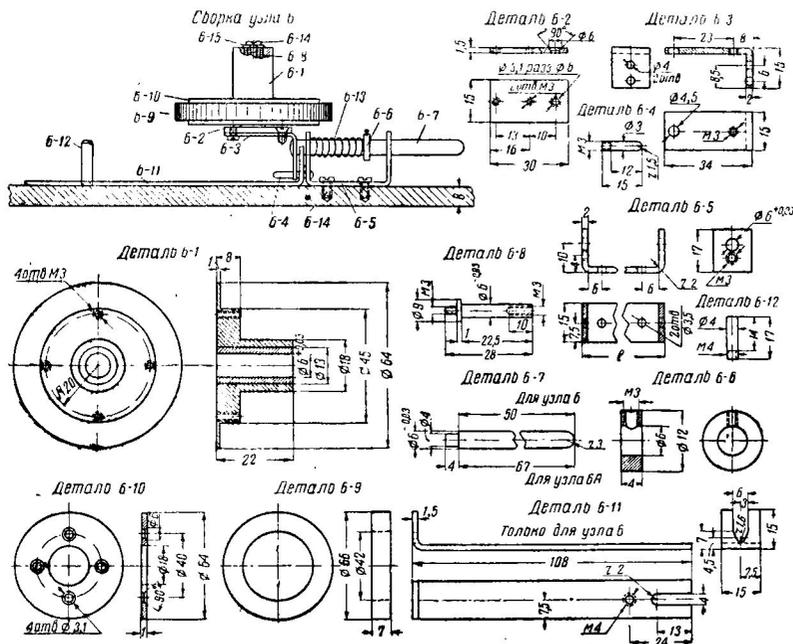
Паразитный ролик рабочего хода (узел 6) и перемотки (узел 6А) и его детали: 6-1—корпус ролика (дюралюминий Д16Т)—1 шт.; 6-2—подвижная площадка (сталь 20)—1 шт.; 6-3—уголок (сталь 20)—1 шт.; 6-4—направляющий стержень (сталь 45)—1 шт.; 6-5—скоба (сталь 20)—1 шт.; для узла 6  $l=32$  мм и для узла 6А  $l=65$  мм; 6-6—кольцо стопорное (сталь 25)—1 шт.; 6-7—стержень (сталь 45)—1 шт.; 6-8—ось паразитного ролика (сталь У8А)—1 шт.; 6-9—кольцо резиновое—1 шт.; 6-10—кольцо (дюралюминий Д16Т)—1 шт.; 6-11—вилка (сталь 20)—1 шт.; 6-12—упор (сталь 45)—1 шт.; 6-13—пружина диаметром 6,5 мм и длиной 45 мм (28 витков проволоки марки Н диаметром 0,5 мм)—1 шт.; 6-14—винт М3×6 мм (сталь 3)—8 шт.; 6-15—шайба (сталь 3)—1 шт. Указанные количества деталей относятся к одному узлу (6 или 6А)
